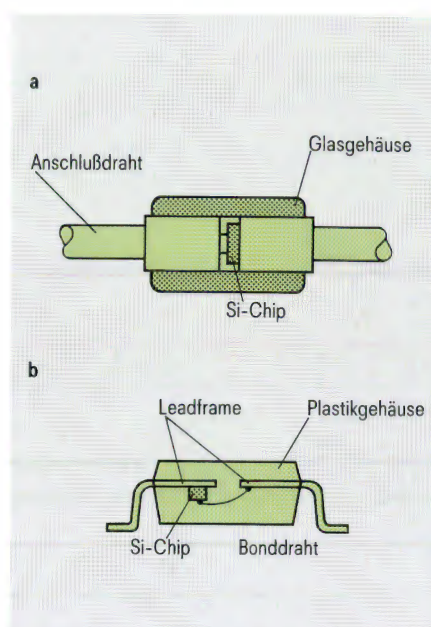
Chip-Montagetechniken im Glasgehäuse (a) und Plastikgehäuse (b)
